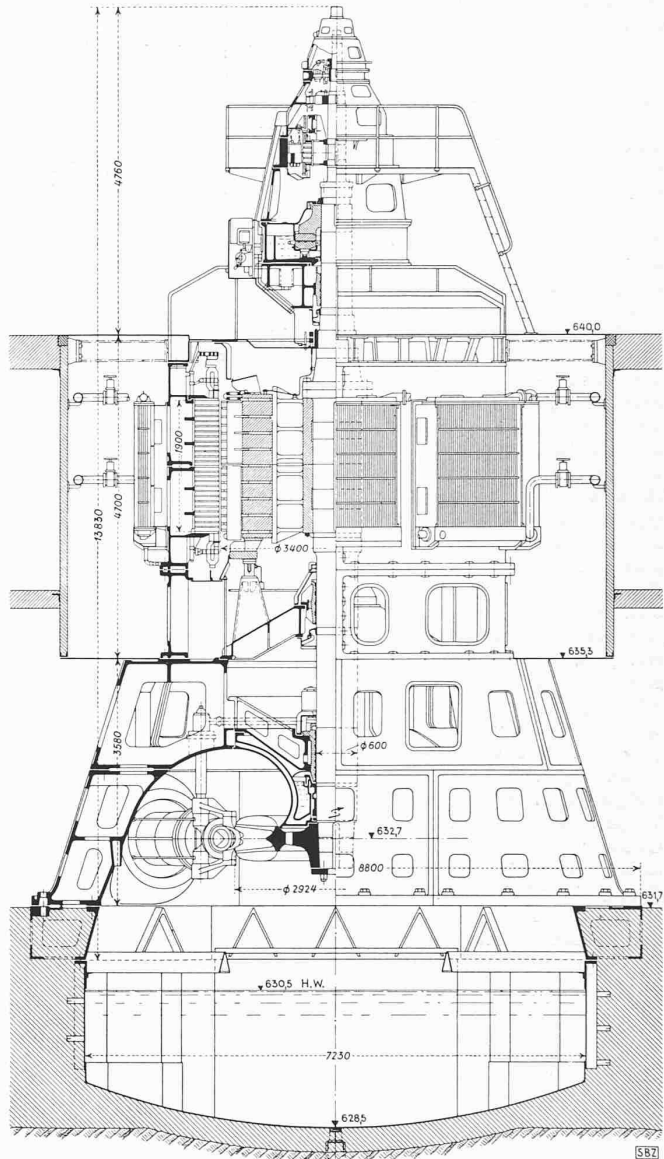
Maschinengruppe des Kraftwerkes Innertkirchen, Schnitt 1:100
